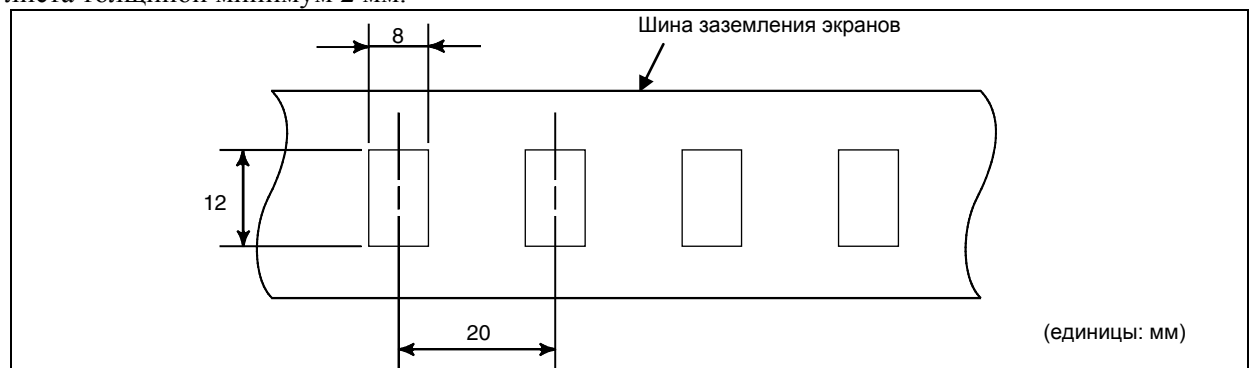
(d) Шина заземления экранов (чертеж отверстий и размеров)
